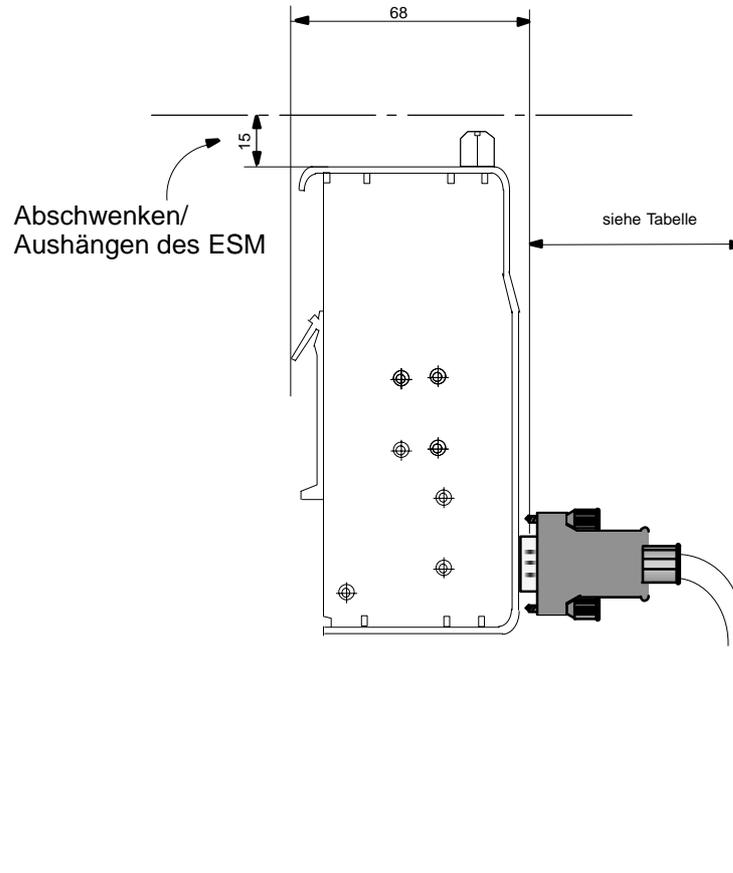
Industrial Ethernet ESM (Seitenansicht; Maße in mm)
